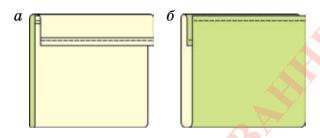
Складывание детали наволочки перед обработкой боковых срезов: а — стачным швом; б — двойным швом
